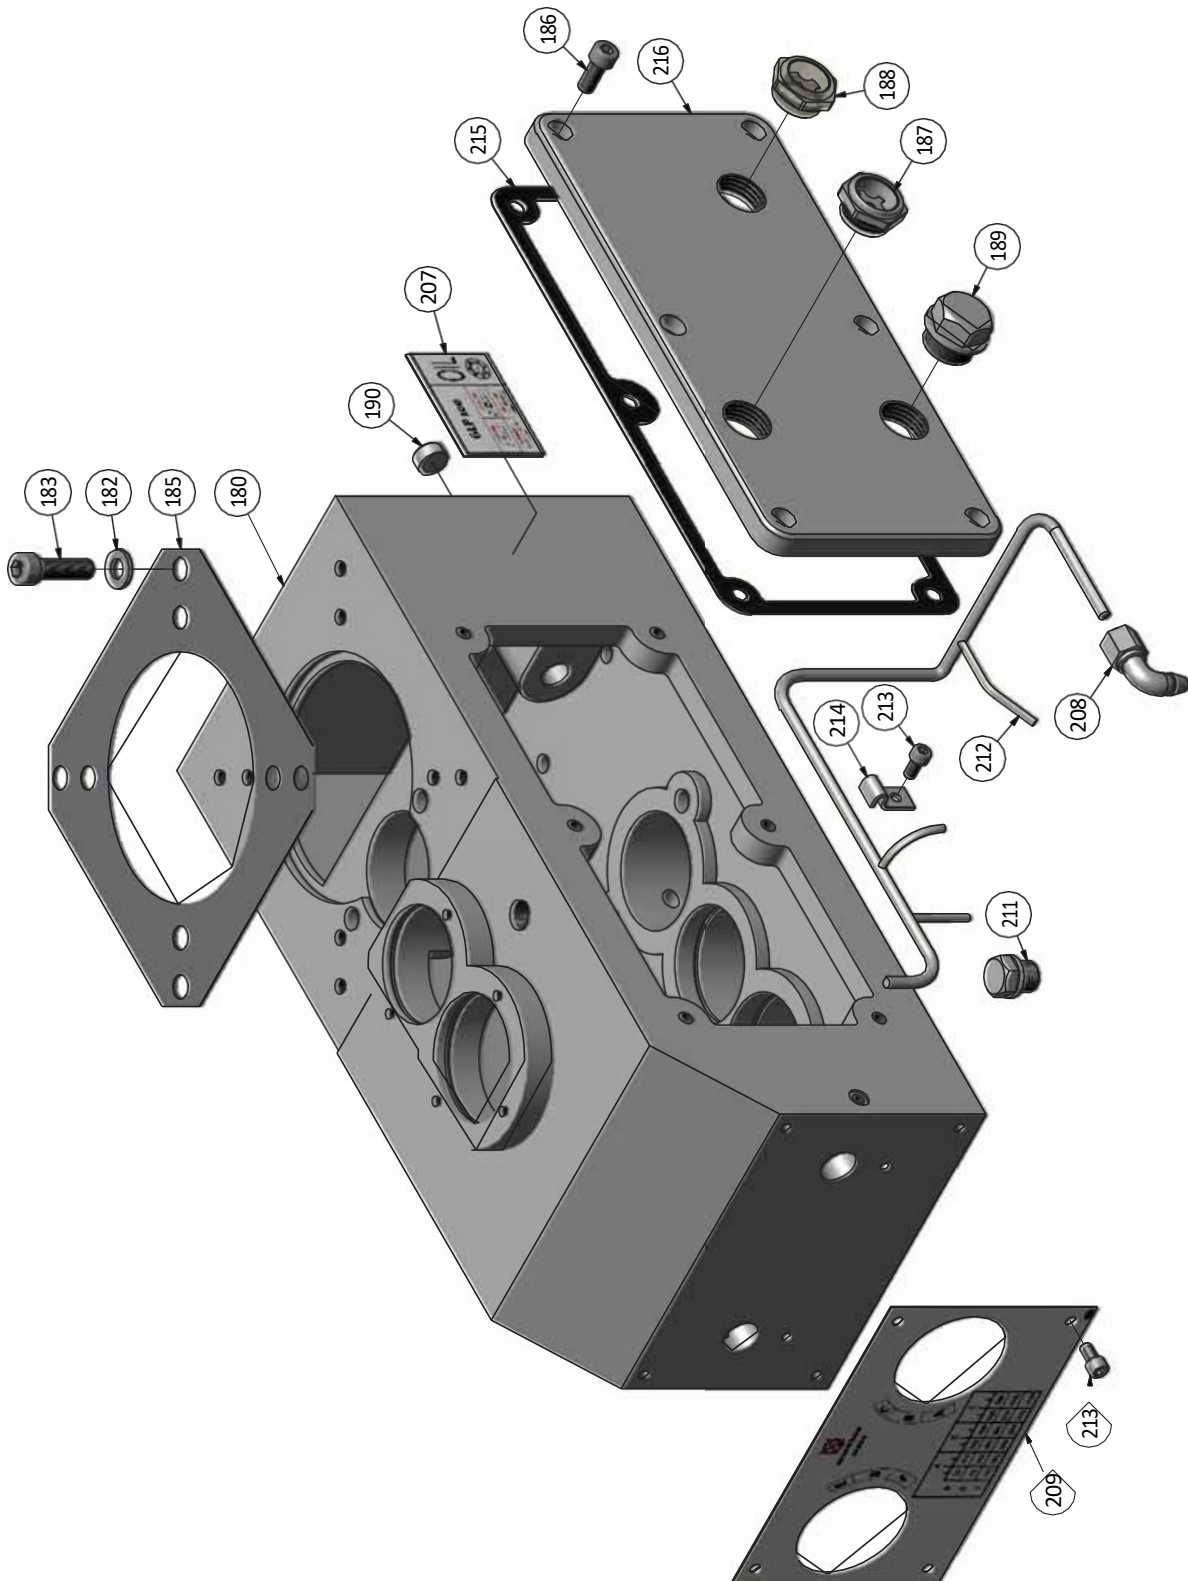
Getriebe Bohrspindel 4 von 4 - Gearbox main spindle 4 von 4
